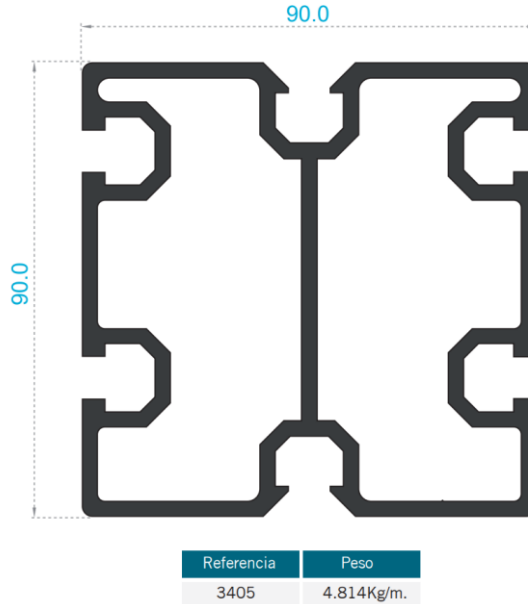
16 Perfil de Aluminio – Propuesto para Viga
